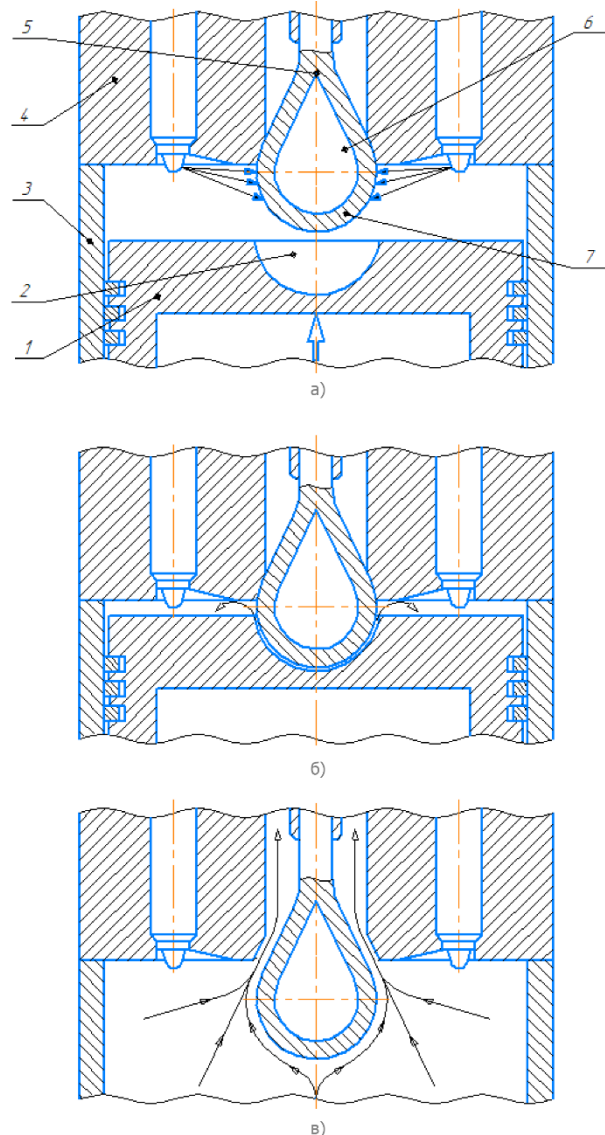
Камера згоряння з плівково – клапанним сумішоутворенням: 1 – головка поршня; 2 – порожнина; 3 – циліндрова втулка; 4 – кришка циліндра; 5 – випускний клапан; 6 – тарілка випускного клапана; 7 – торцева частина тарілки
